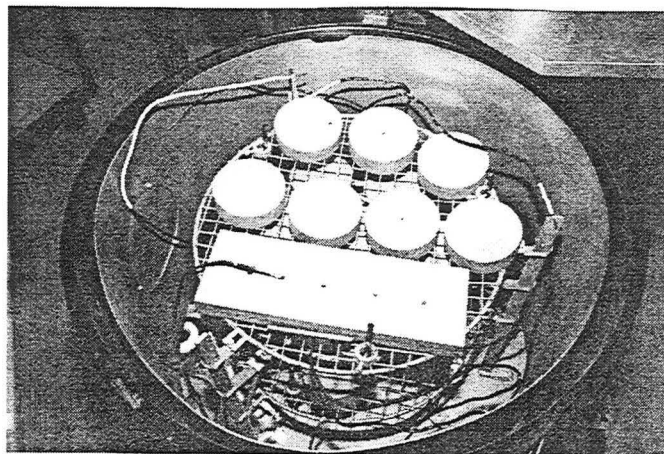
Chargement des pièces et éprouvettes en configuration pleine.
